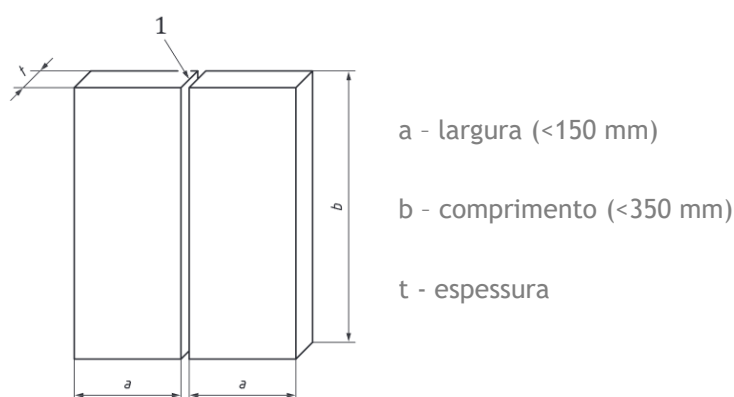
Provede de teste para soldadura topo a topo em chapa com penetração completa [50]
